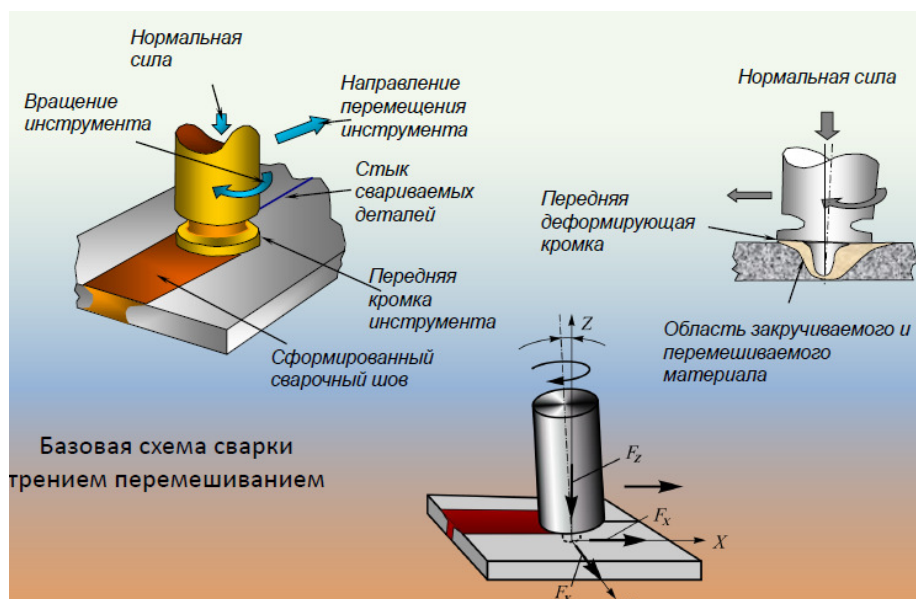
Схема процесса сварки трением с перемешиванием: F_x , F_y , F_z —усилия, действующие инструмент вдоль осей x , y , z соответственно
